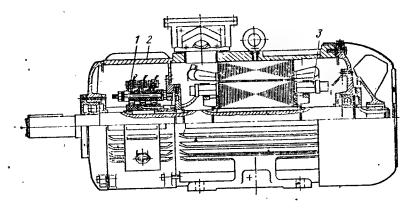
Асинхронный двигатель с фазным ротором 4AK250. 1— узел контактных колец; 2— станина; 3— обмотка ротора.
